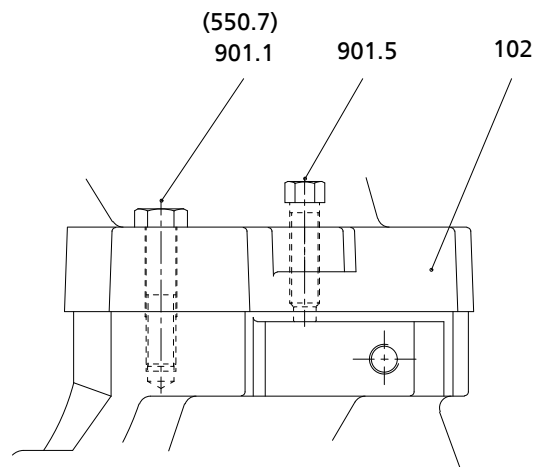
Деталировочный чертеж: Резьбовое соединение фланца
